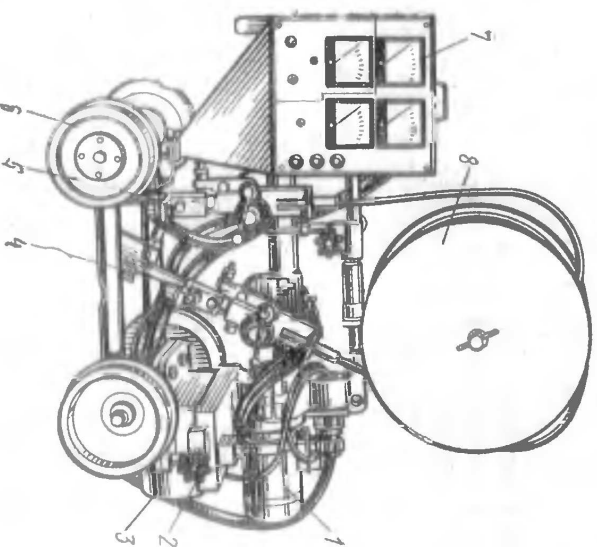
Трактор ТС58 для двухдуговой сварки под флюсом:
